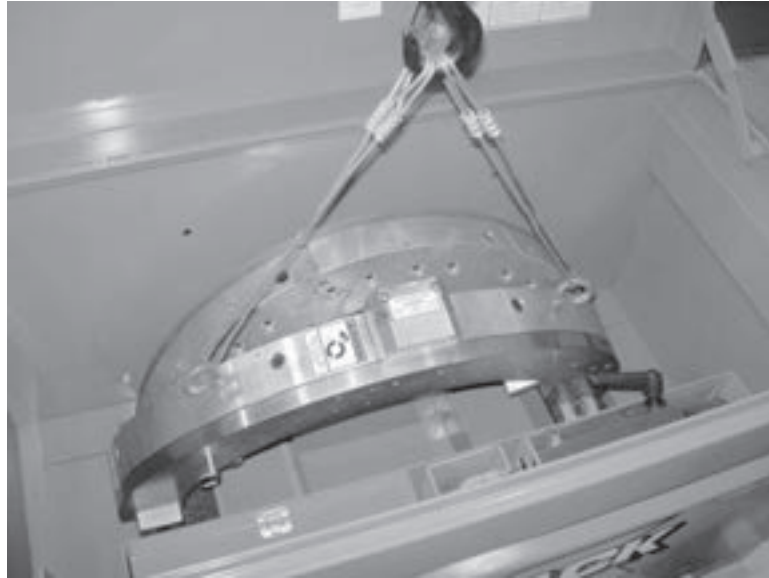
Use un dispositivo de elevación para elevar cada mitad de la máquina fuera de la caja de almacenamiento.
